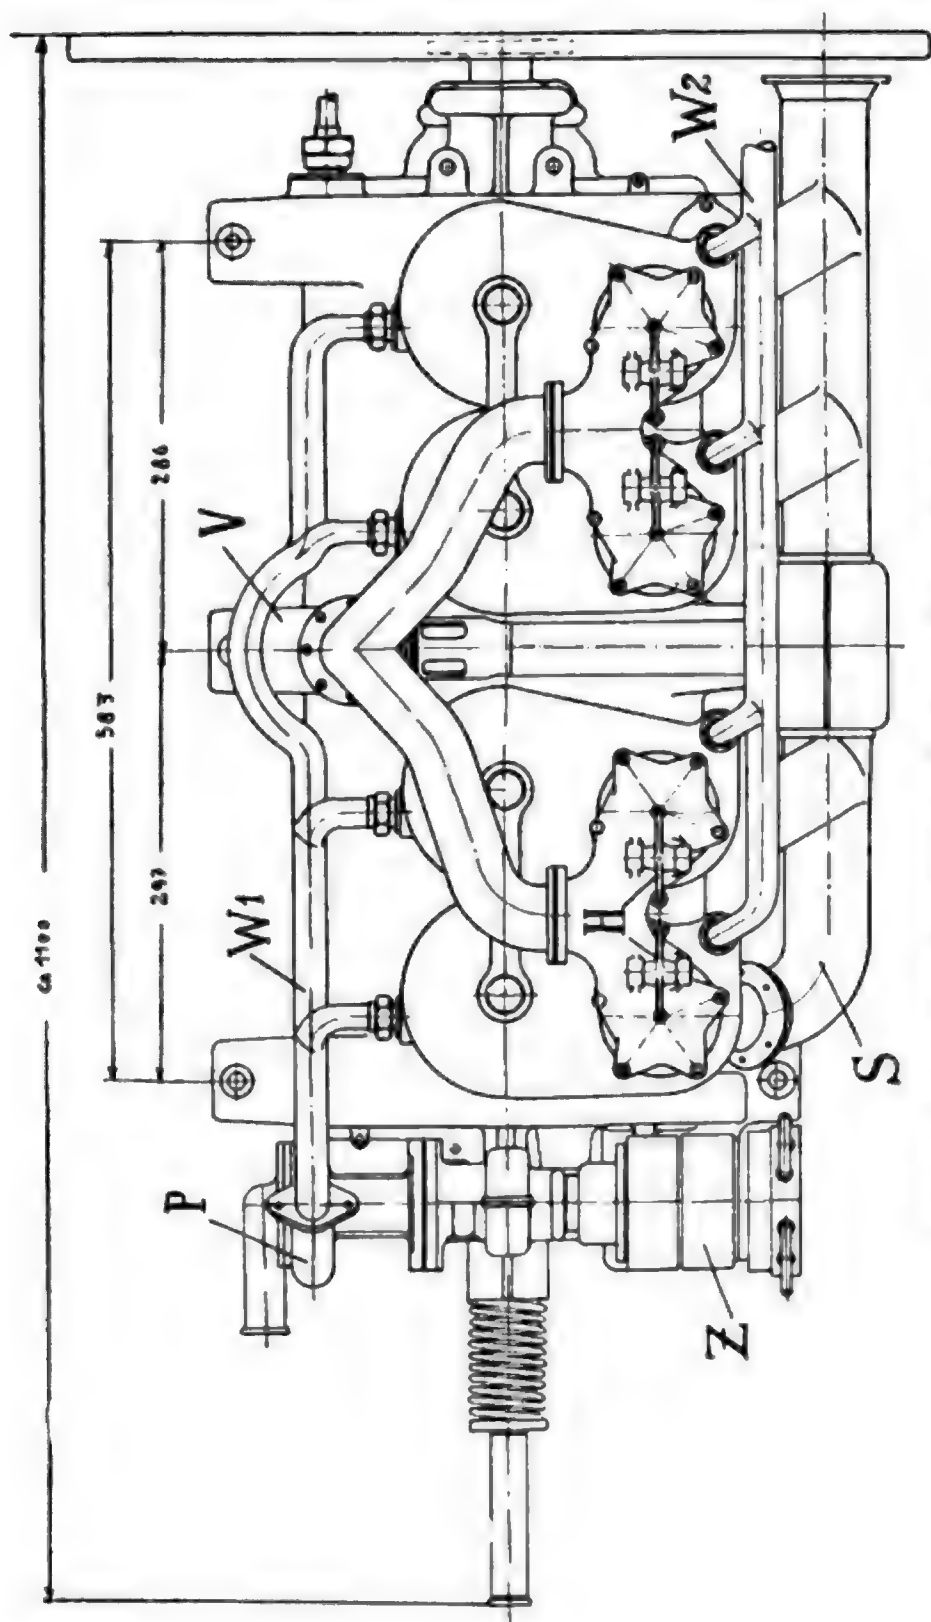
Zeichnung des Flugmotors von Körtling, Ansicht von oben.
